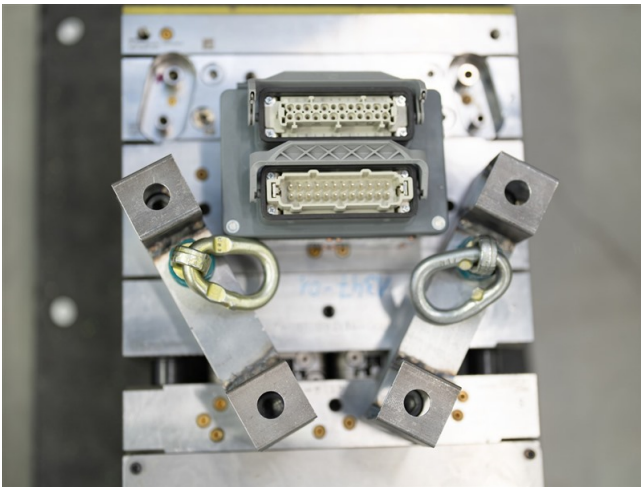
Spritzgusswerkzeug mit montierter Werkzeugbrücke und drehbaren Hasco-Ringschrauben
